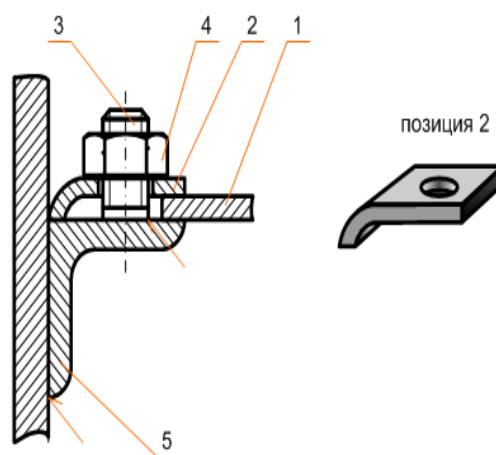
Крепление полотна тарелки вдоль корпуса
